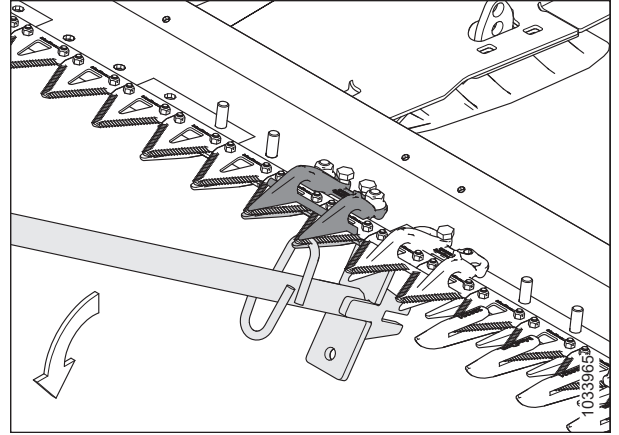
Регулювання вниз — короткий протиріжучий палець
